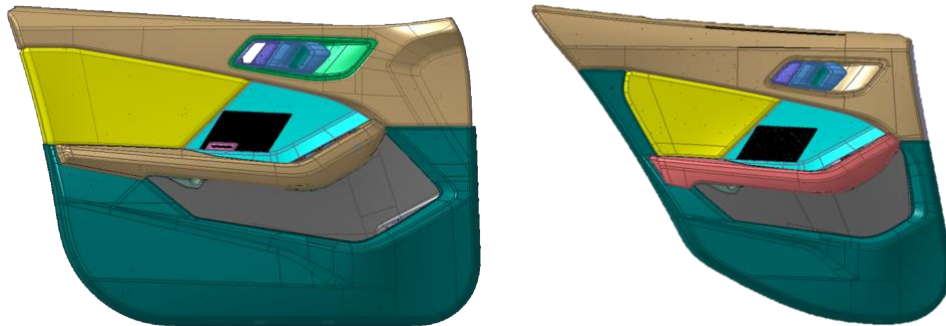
Paneles de puerta del BMW F70 (Serie 1) a desarrollar en el proyecto
